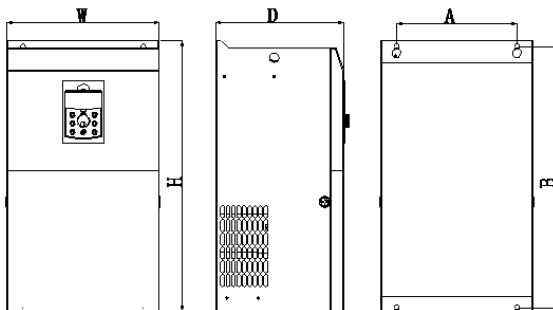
380V (4T) 45~132kW 变频器外型尺寸及安装尺寸示意图
